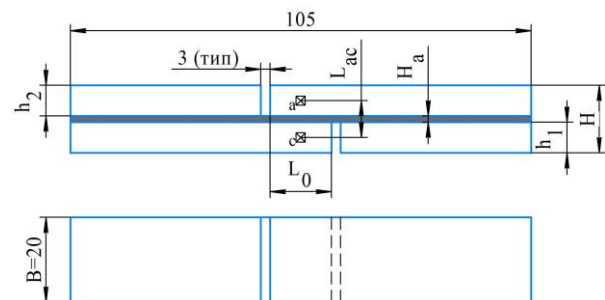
Загальний вид зразка клейового з'єднання внапуск для визначення модуля зсуву
